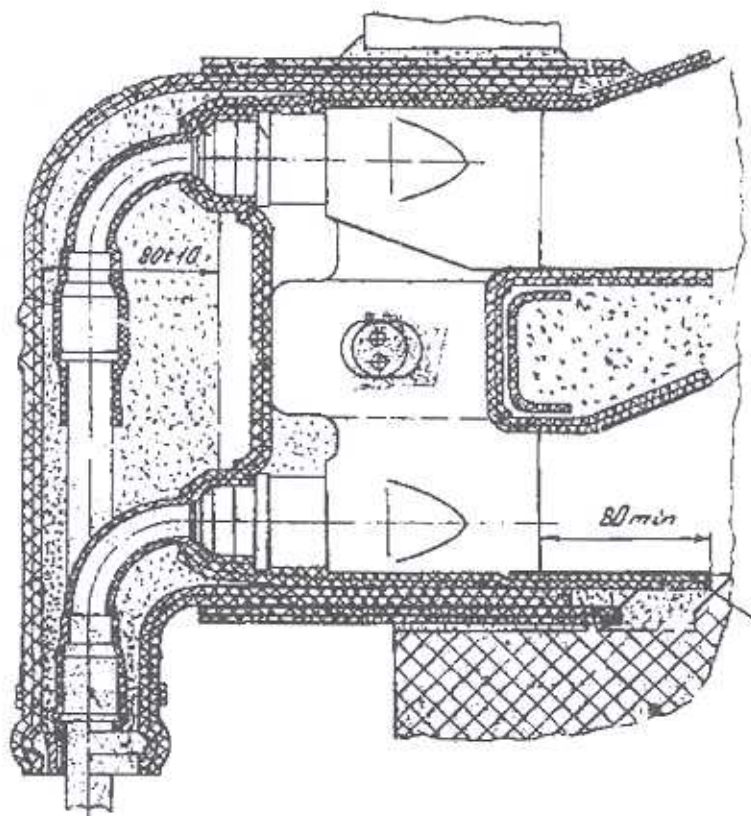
Изолировка контактного соединения стержней обмотки статора
